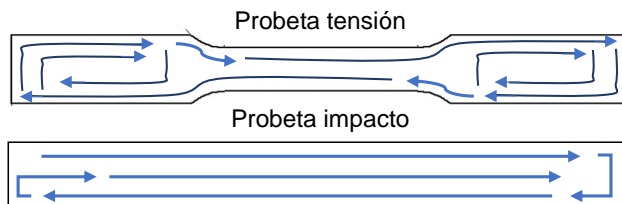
Proceso de vaciado en el molde para Tensión e impacto
